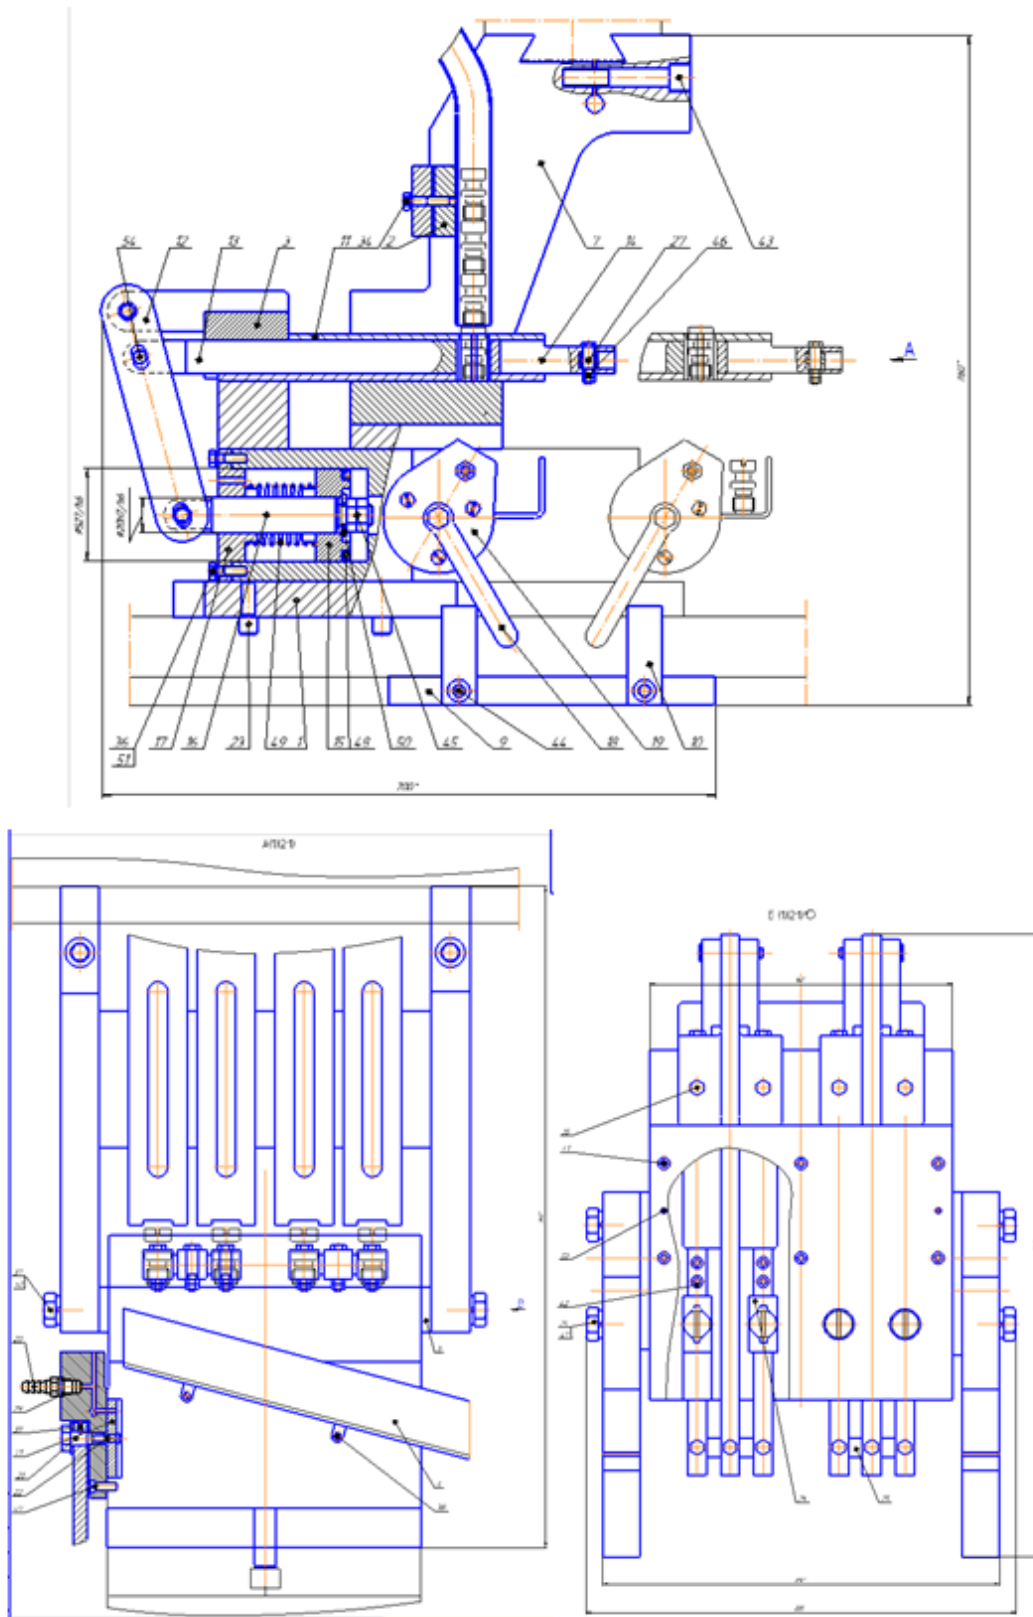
Автоматизована система оброблення шліцевого пазу фрезеруванням
